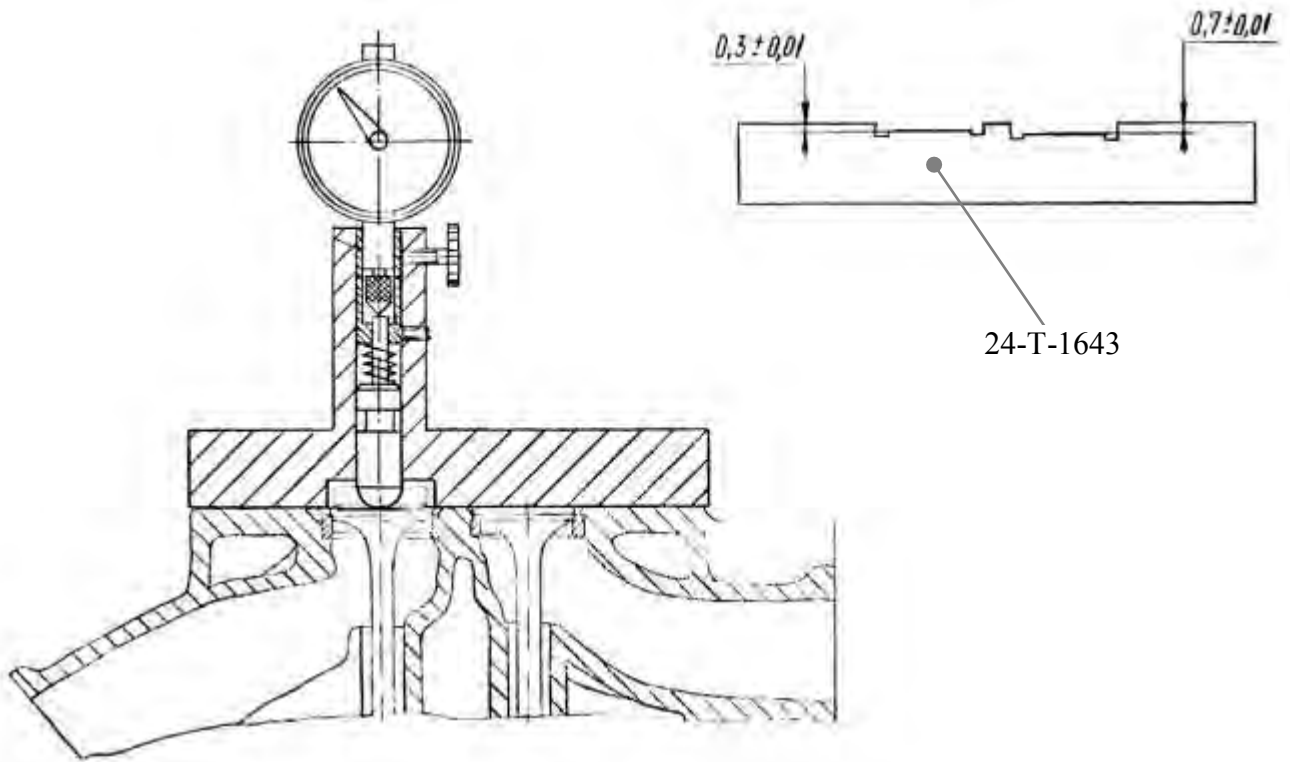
24-Φ-74760 Калибр измерительный
